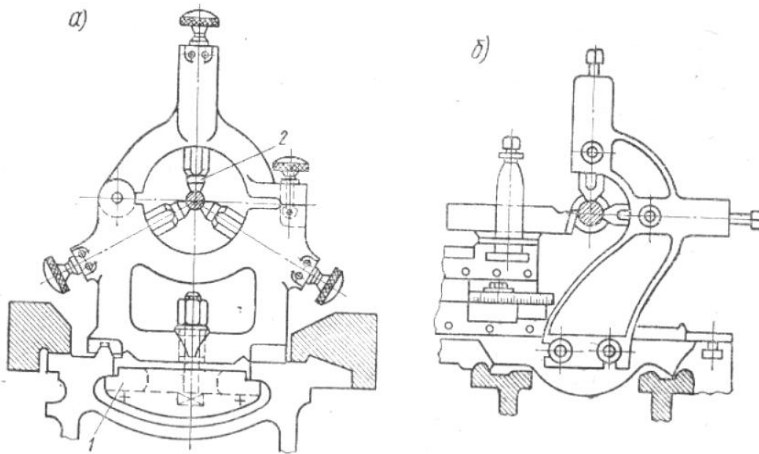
Люнеты: а) –неподвижный; б) подвижный; 1-планка крепления к направляющим станины(салазкам); 2- кулачок
